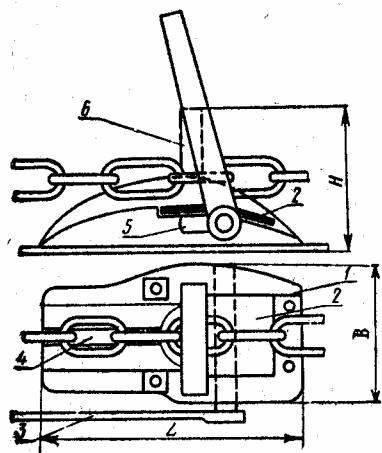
Палубный кулачковый стопор (стопор Легофа):
